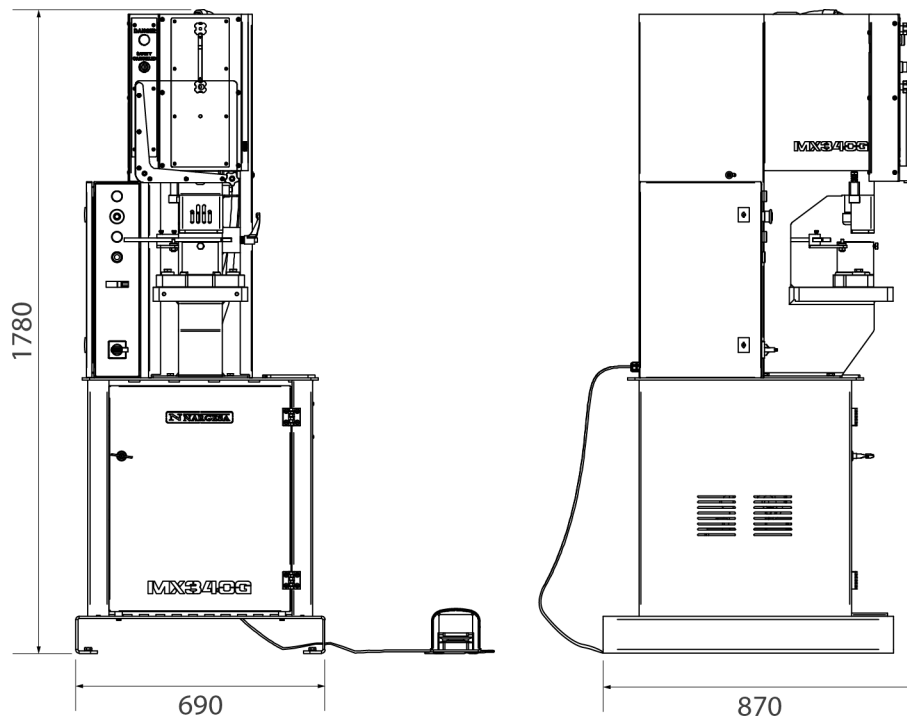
Dimensiones exteriores de la punzonadora MX340G
